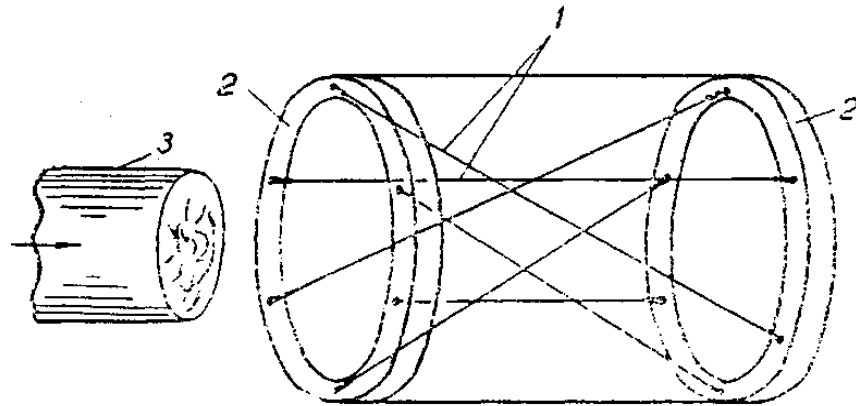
Окорочное устройство с туго натянутыми, перекрещивающимися стальными канатами: 1 - корообдирочные элементы; 2 - кольца; 3 - обрабатываемый лесоматериал [53]
